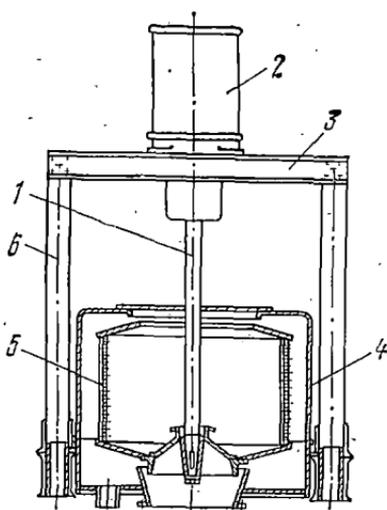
Схема центрифуг типа ФПН, ОПН и ФПД
